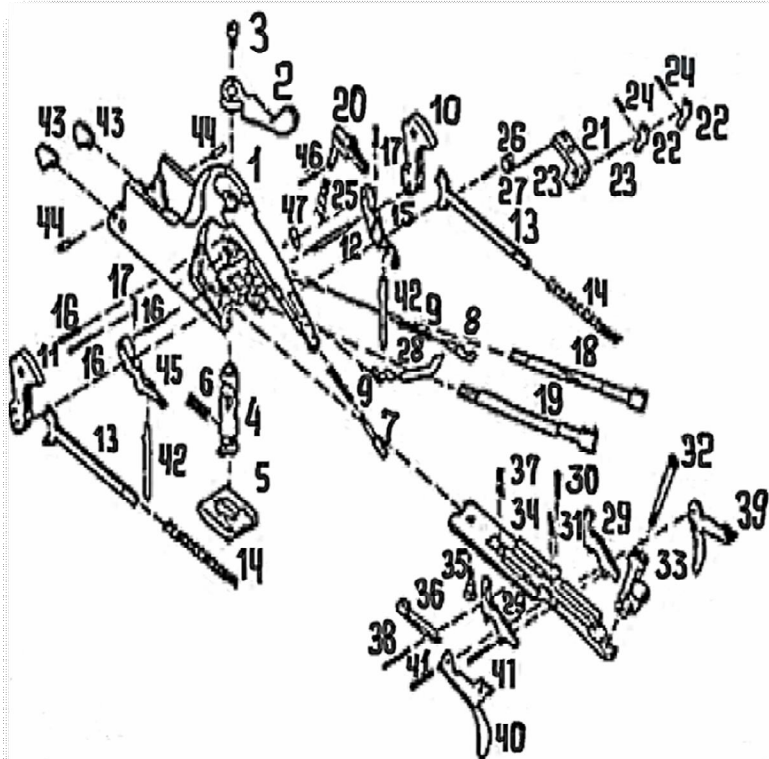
Коробка – (1), рычаг запора – (2), винт – (3), ось рычага запора – (4),
